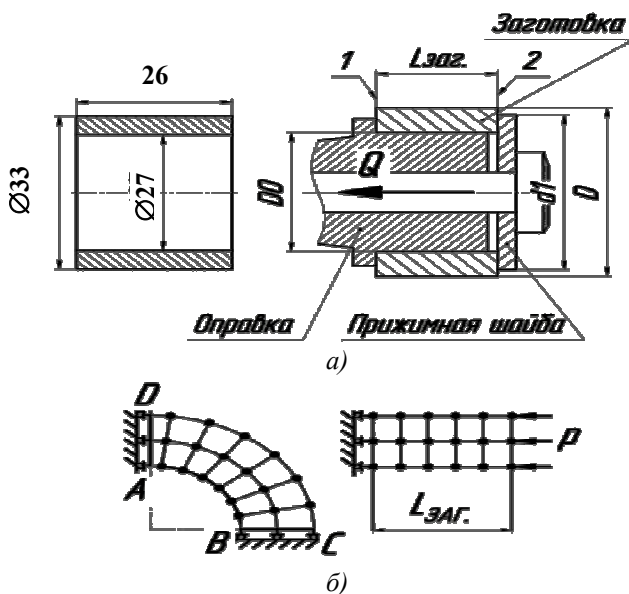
Расчетная схема: а – схема закрепления заготовки; б – граничные условия
